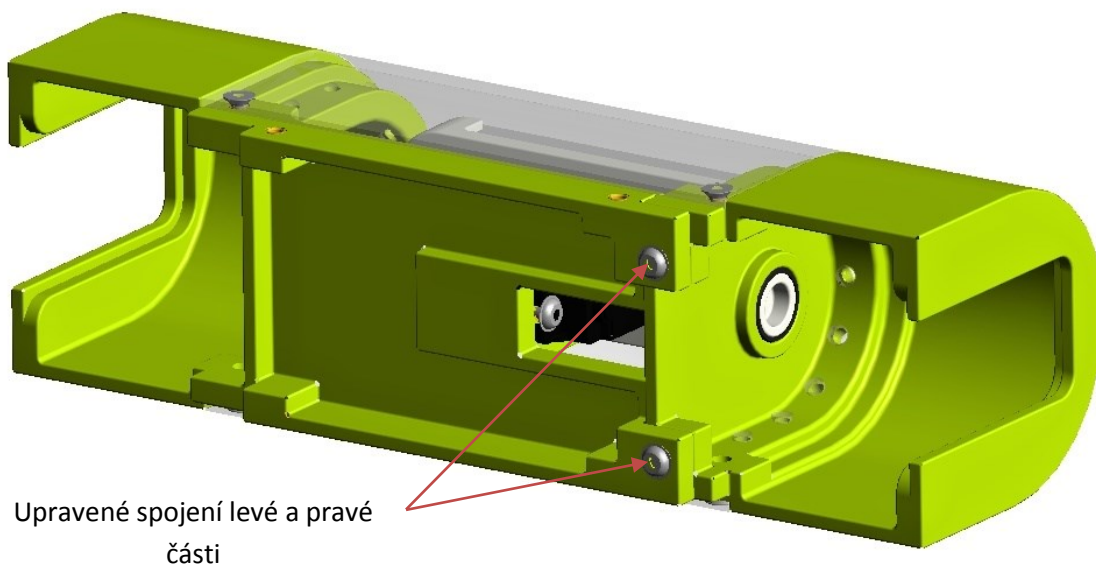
Robot – 3. Stádium – Zadní blok
